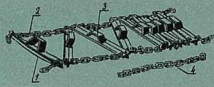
Гусеничная цепь противоскольжения: 1 — трап; 2 — межтрансовая цепь; 3 — соединительное кольцо; 4 — серга; 5 — соединительный паук; 6 — гребень трапа; 7 — соединительная цепь.
